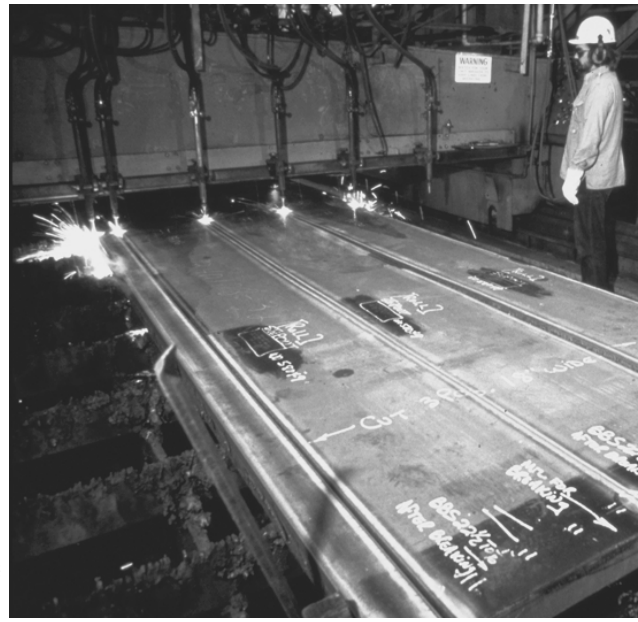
• Corte de planchas de acero con soplete automático en un taller de fabricación.
